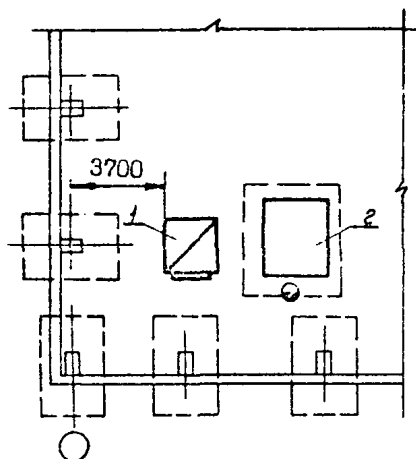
Схема расположения участка ковочных молотов с МПЧ 150-5000 кг с нагревательными камерными печами (верхнее или нижнее дымоудаление):
